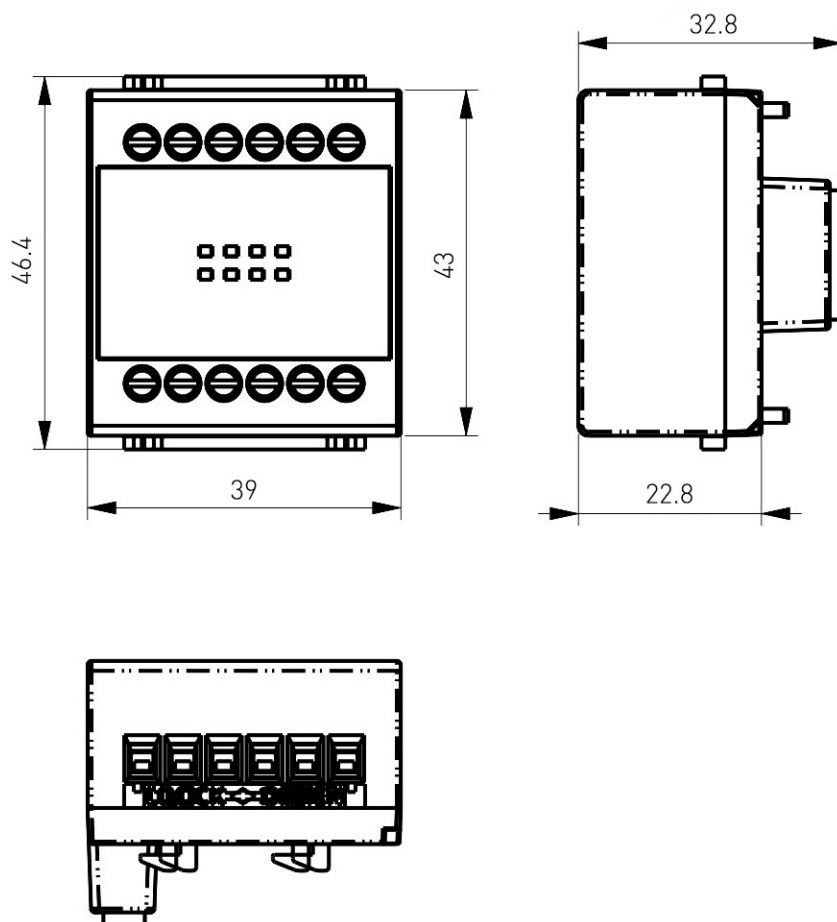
Габаритный чертеж модуля расширения серии F.
